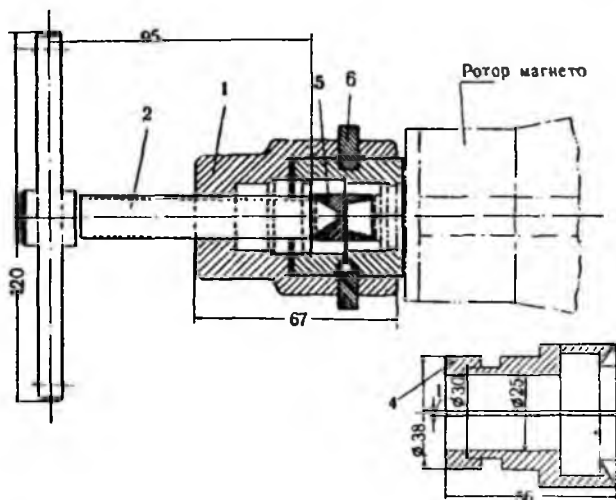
Съемник внутренних колец шарикоподшипников и малой шестерни с ротора магнето СС-4.
